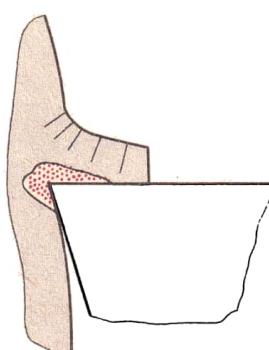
Schneidenaufbau drückt sich ins Werkstück ein
